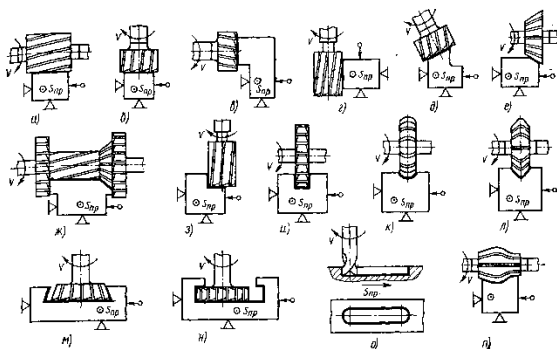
Схемы обработки заготовок на горизонтально-и вертикально-фрезерных станках
